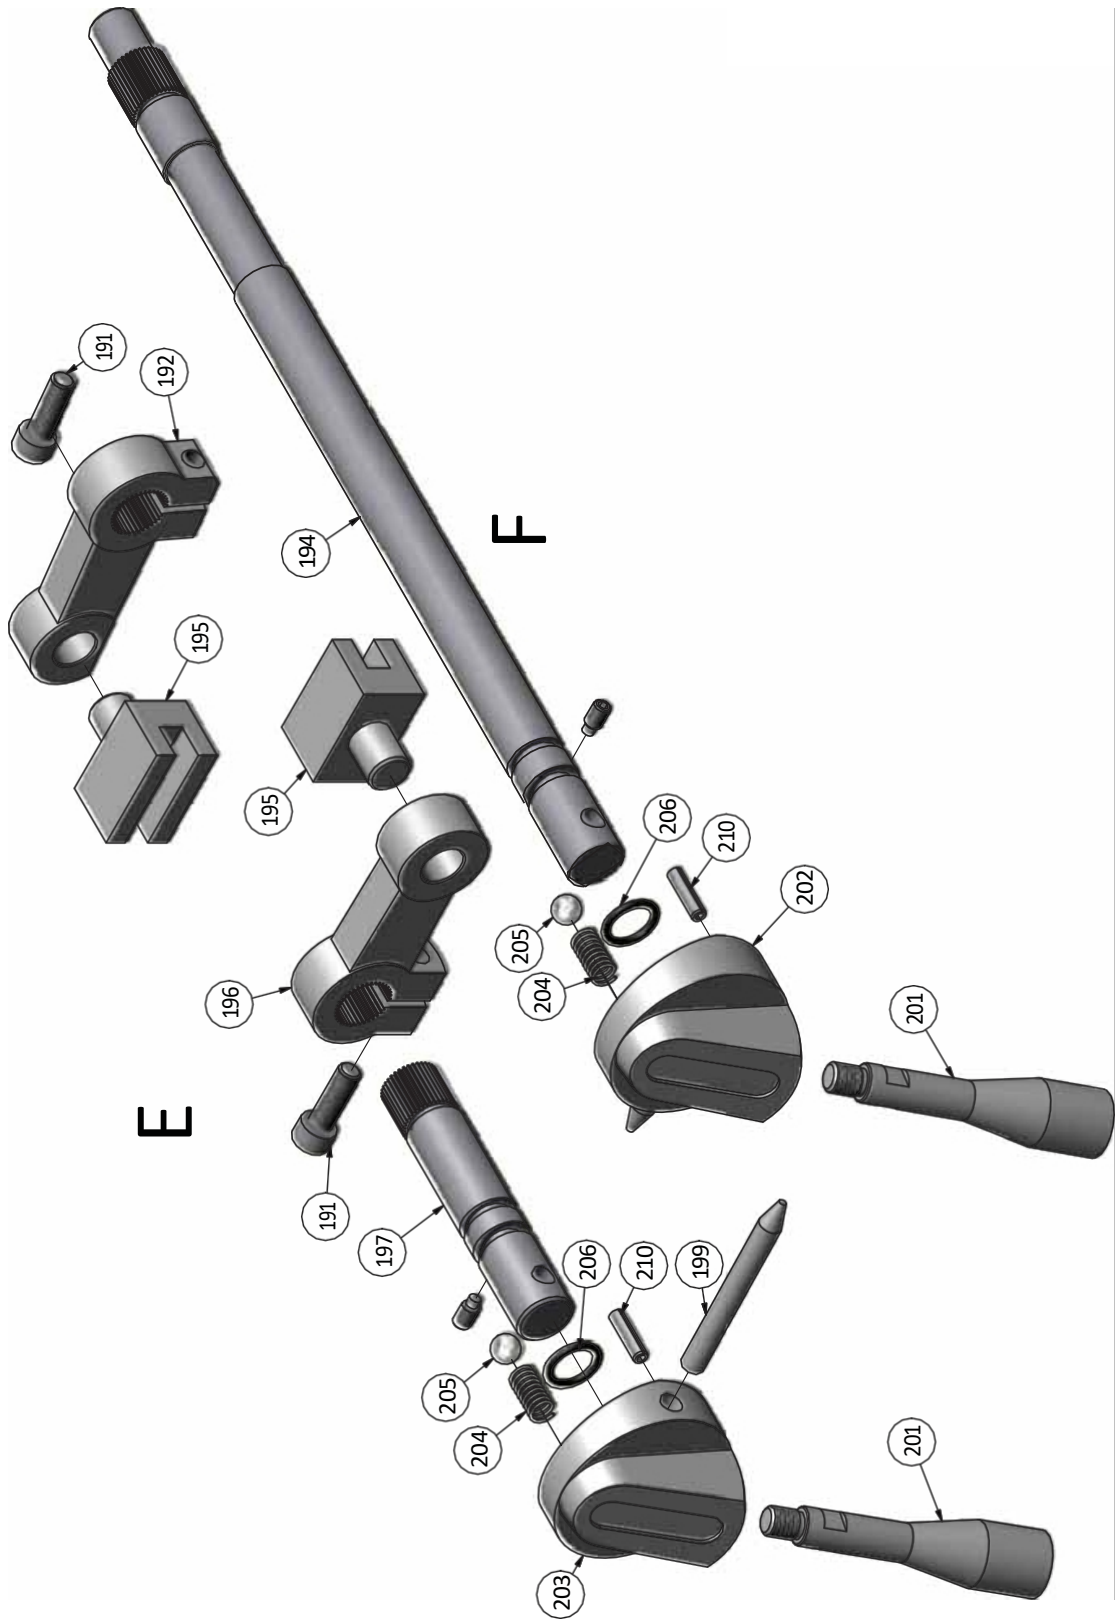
Getriebe Bohrspindel 3 von 4 - Gearbox main spindle 3 von 4
